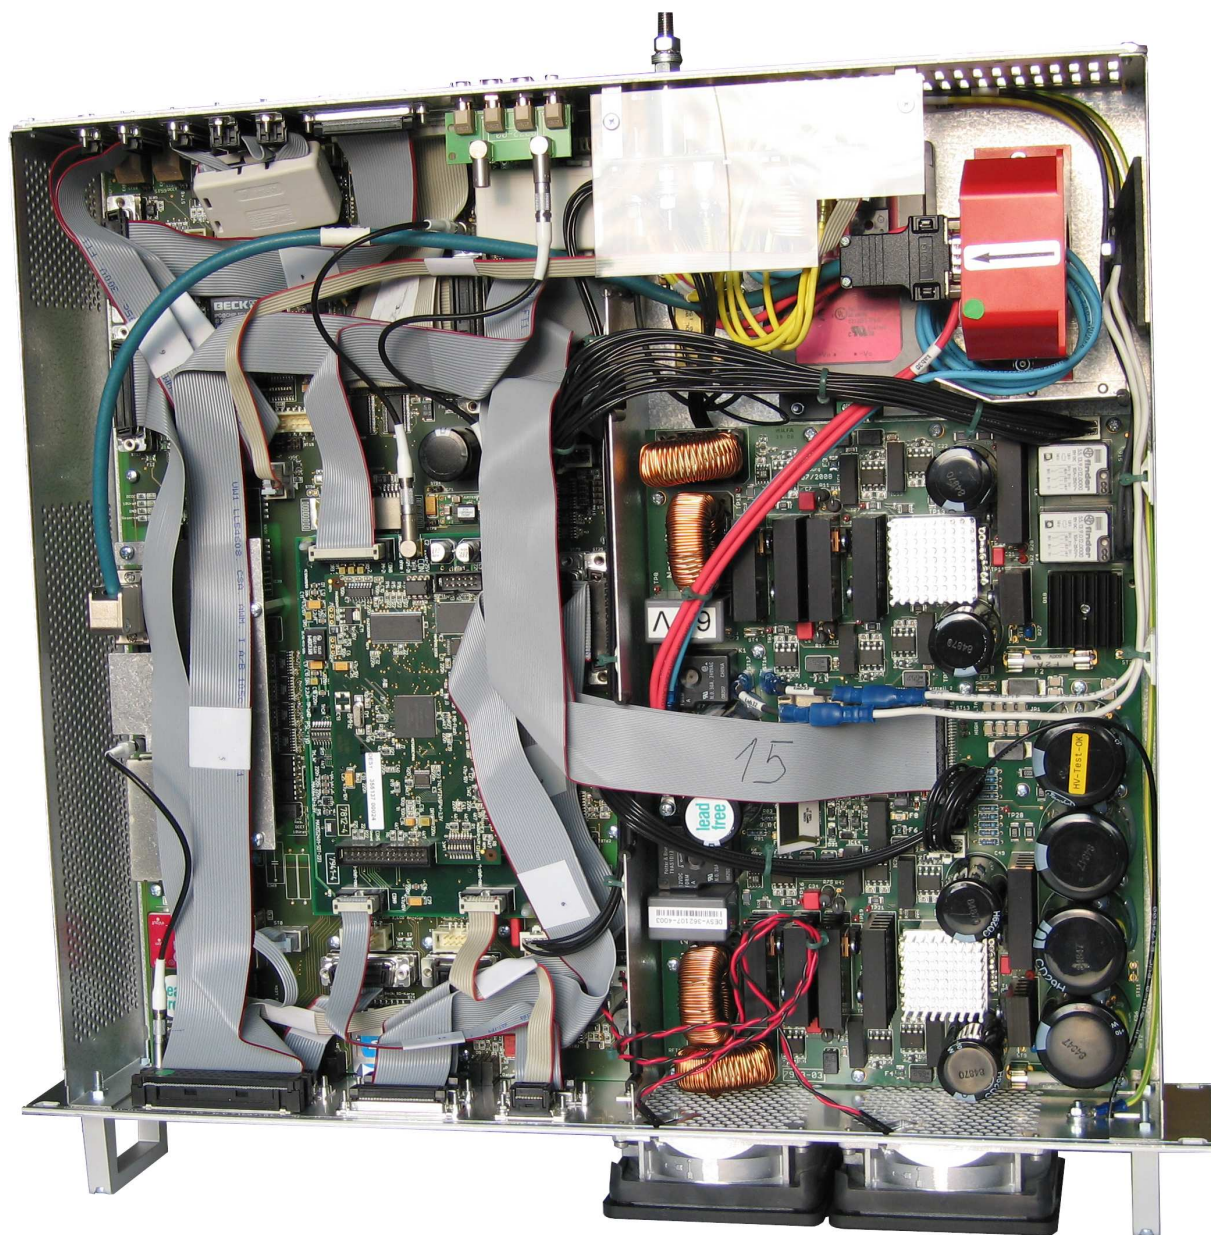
Sicht auf die einzelnen Baugruppen des Korrekturnetzteils – beim Regler für Choppernetzteile fehlt die rechte Baugruppe.
